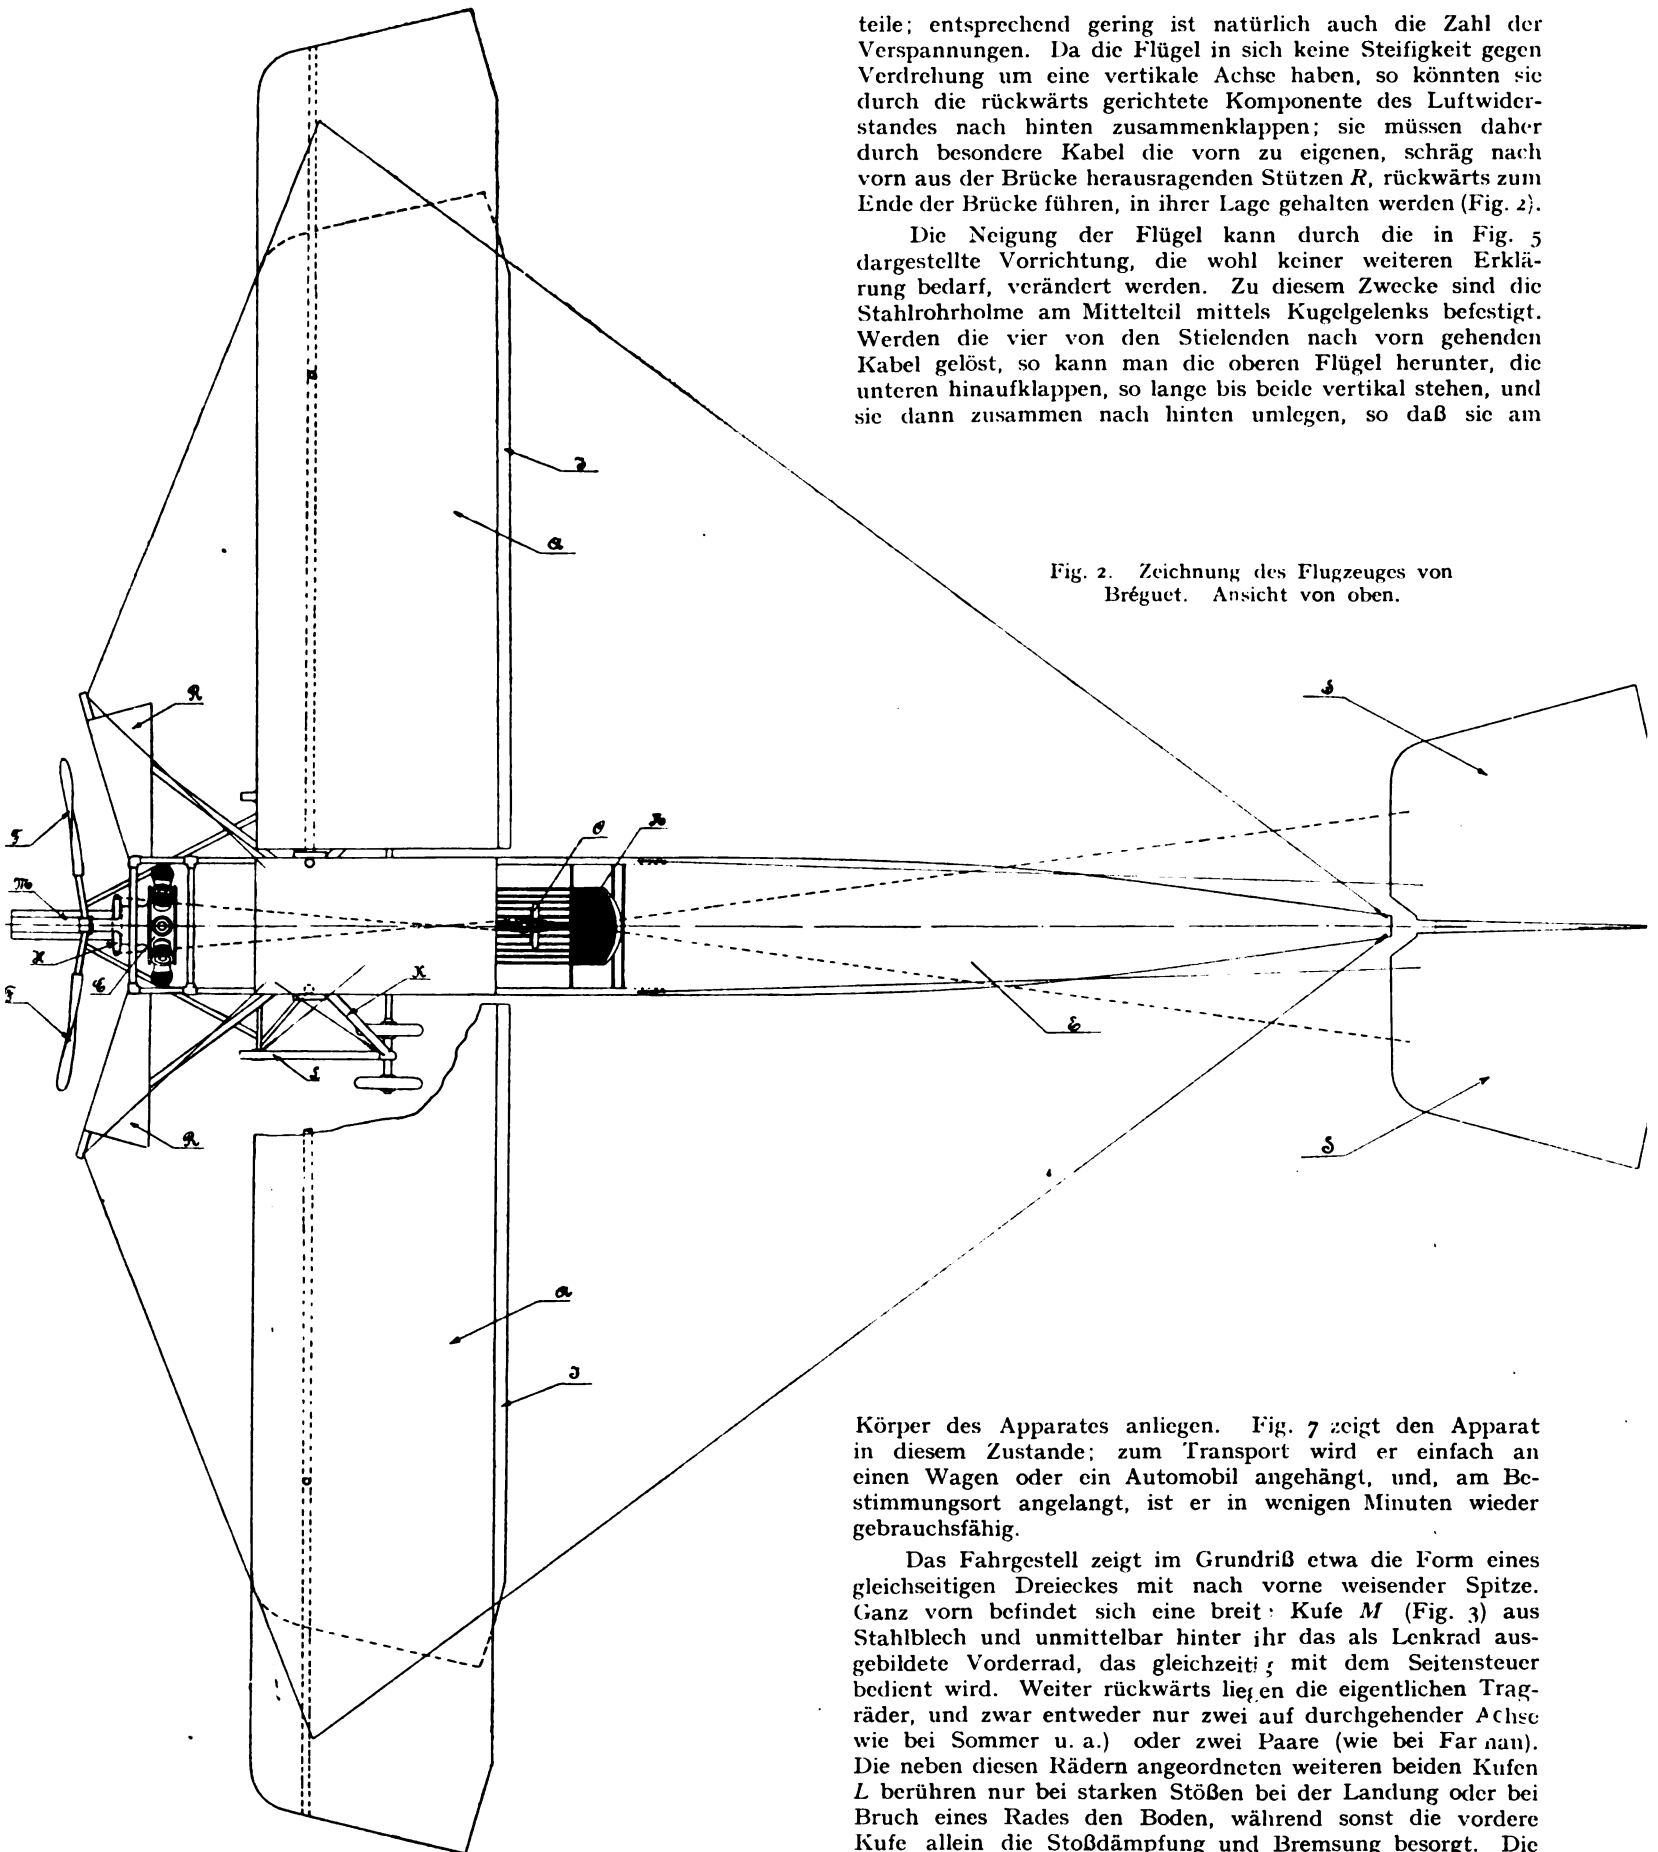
Zeichnung des Flugzeuges von Bréguet. Ansicht von oben.
